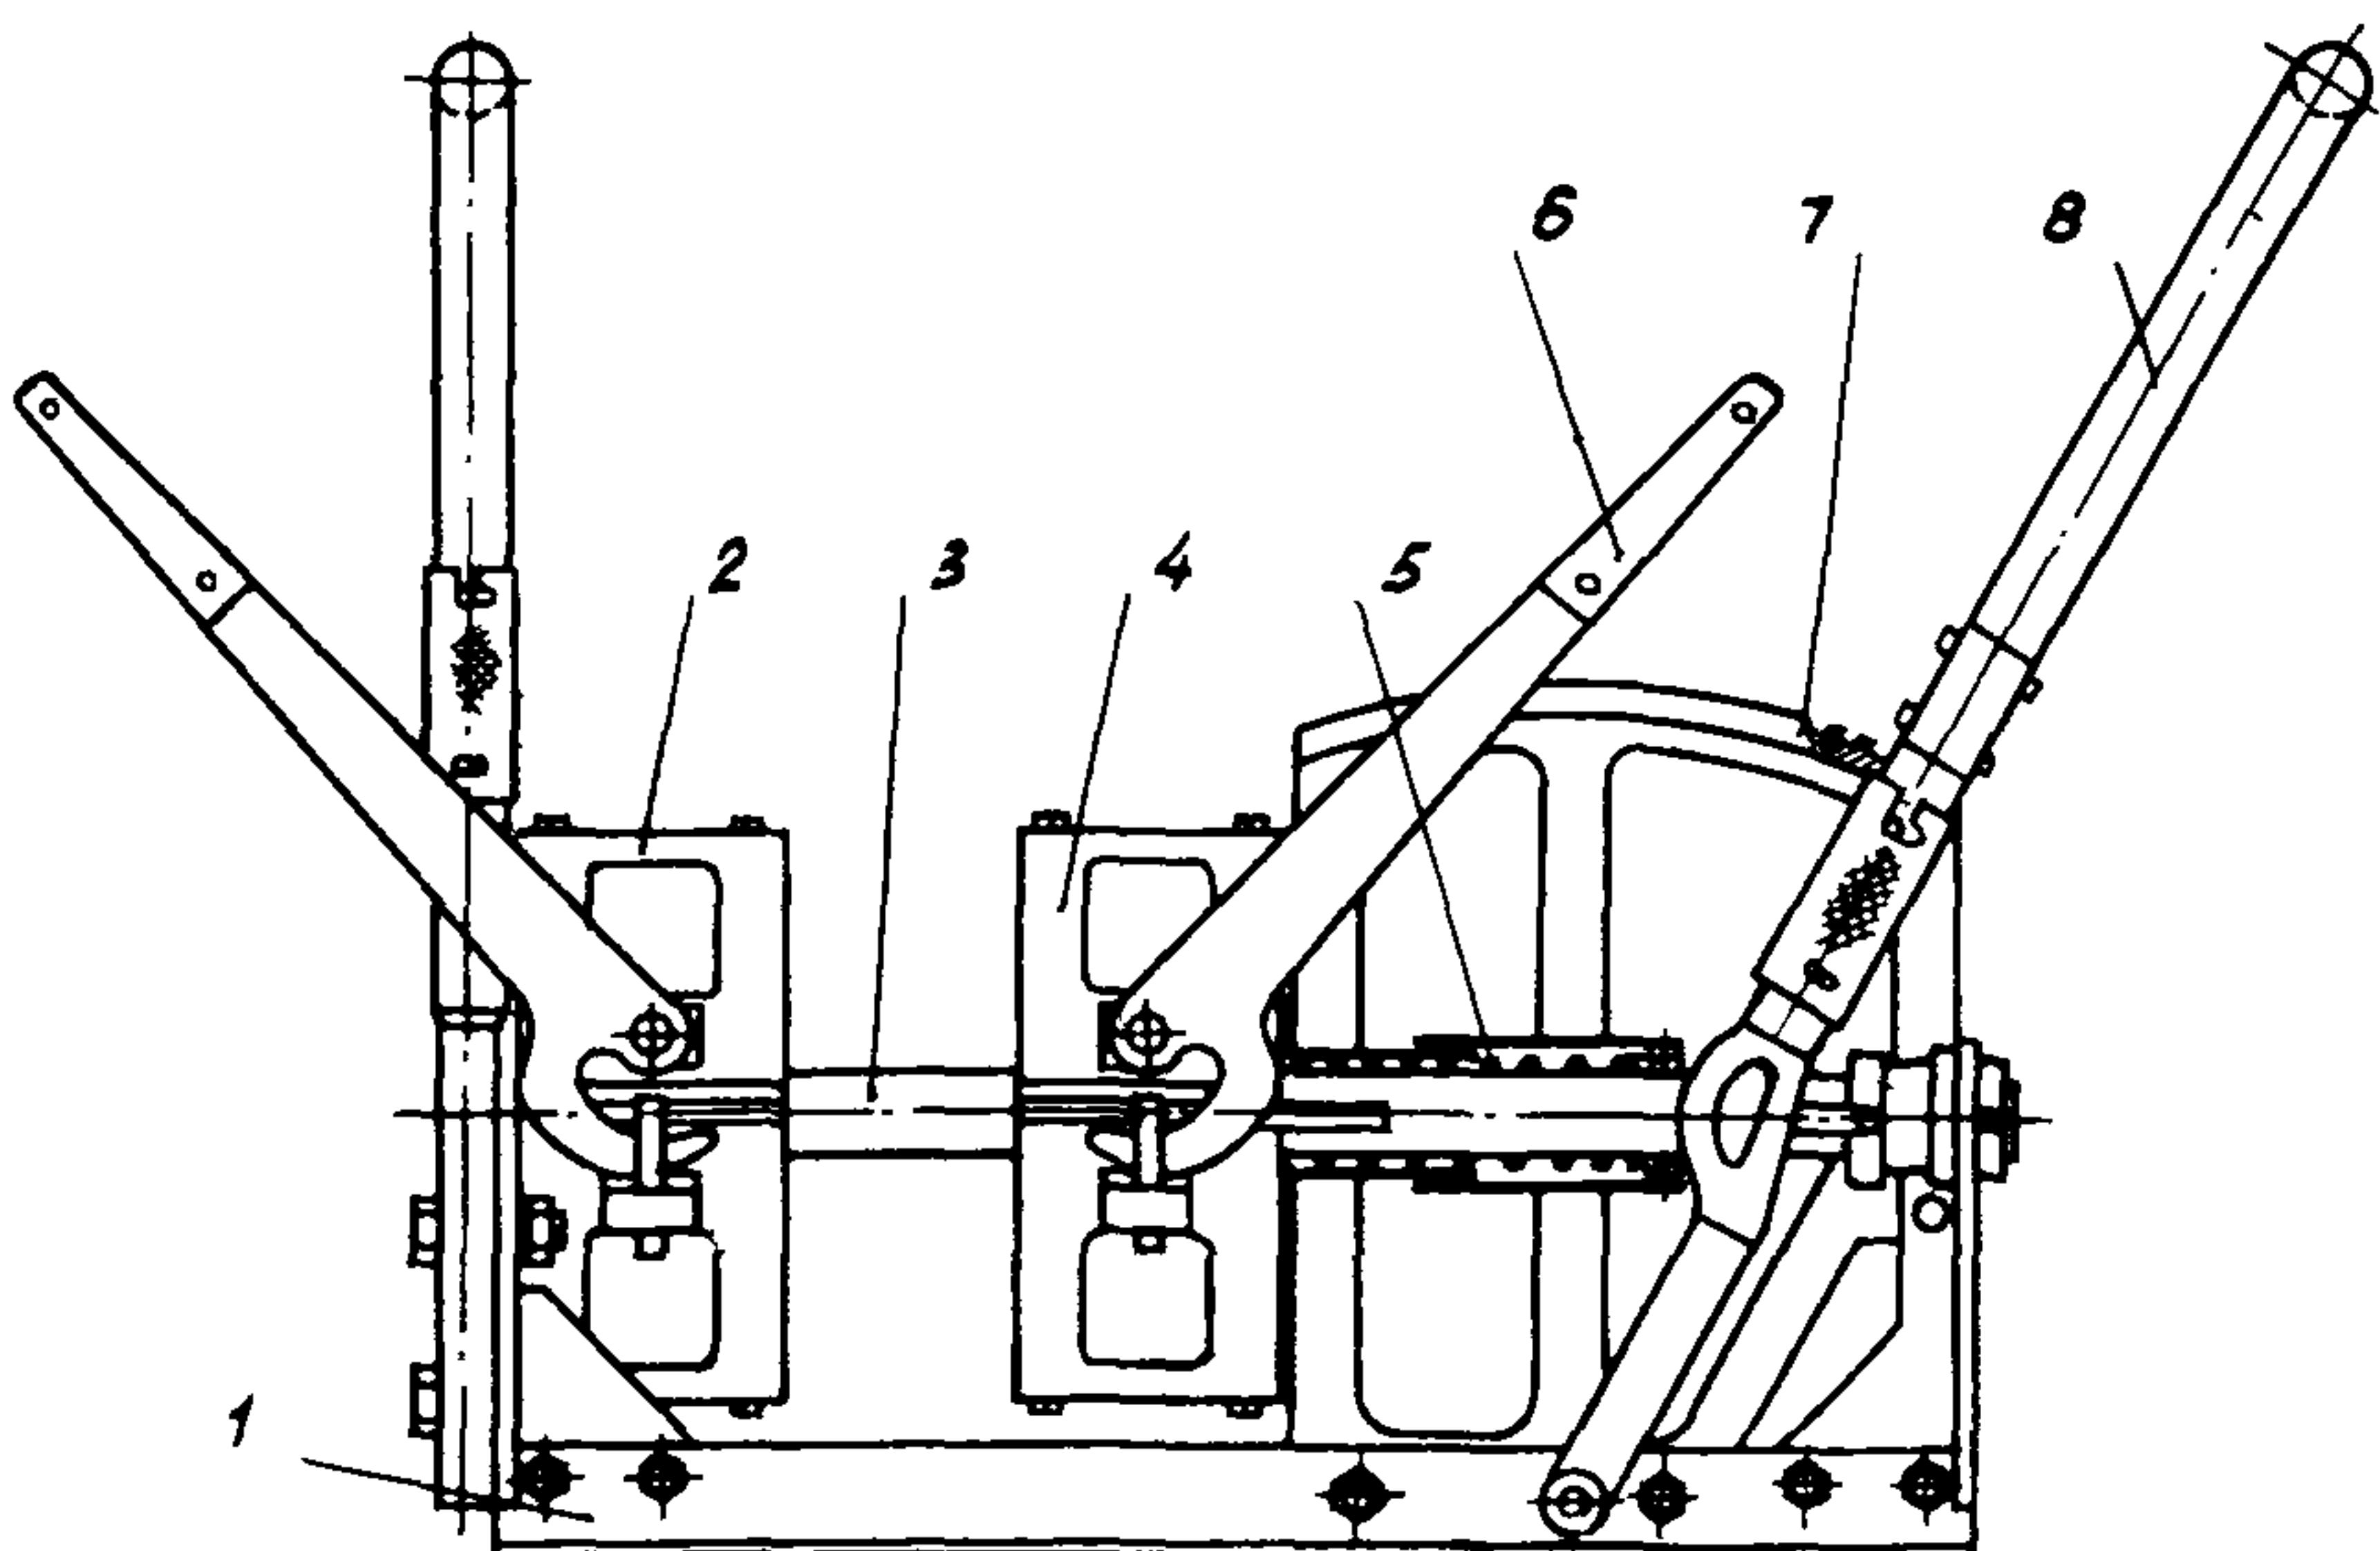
Схема устройства для центровки и сварки встык полиэтиленовых труб диаметром 110–160 мм:
